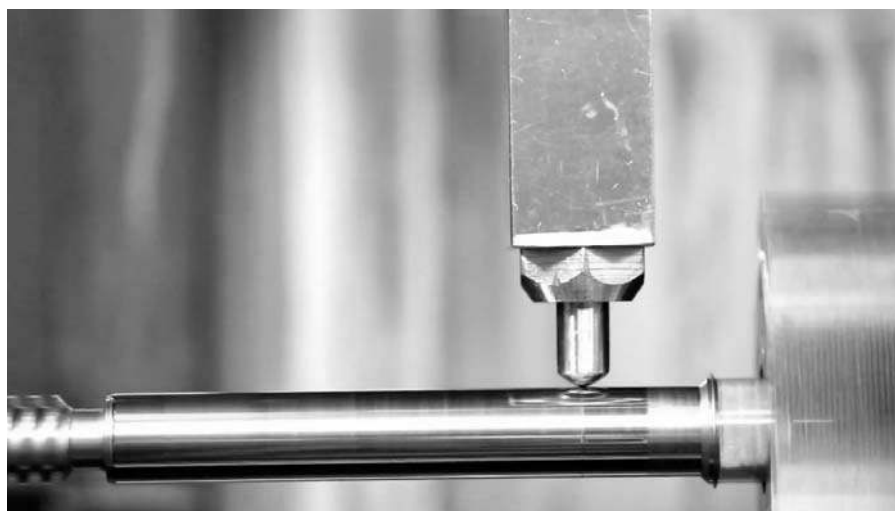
Применение алмазного выглаживателя для обработки детали
